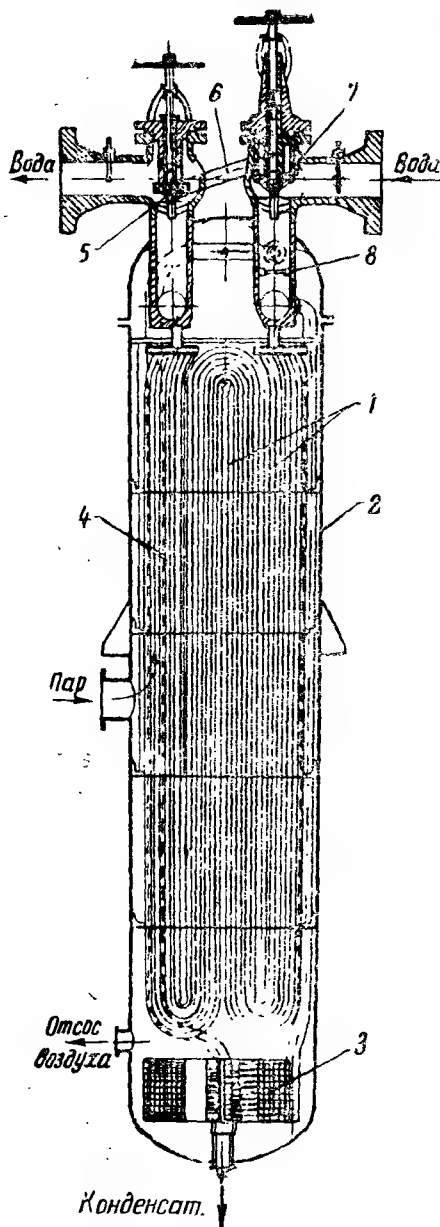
Подогреватель высокого давления типа БИП с встроенным охладителем дренажа. 1—образные трубки; 2—корпус; 3—спиральный охладитель, 4—отсек для использования перегрева пара; 5—выходной автоматический клапан, 6—перепускная труба, 7—входной автоматический клапан, 8—диафрагма
